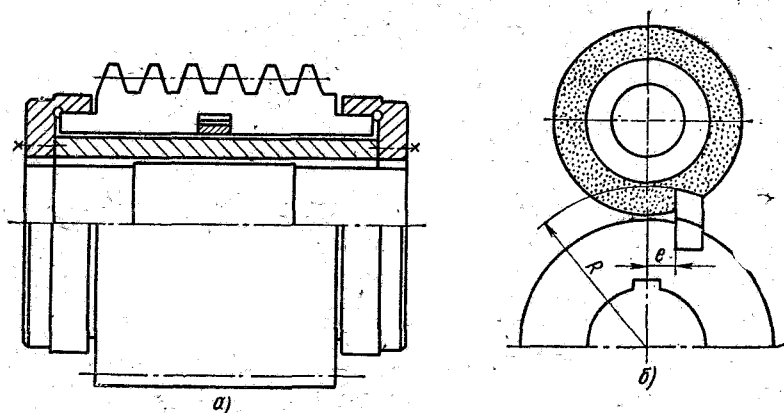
Сборная незатылованная червячная фреза со вставными рейками: а — общий вид; б — схема установки рейки в приспособлении при заточке
